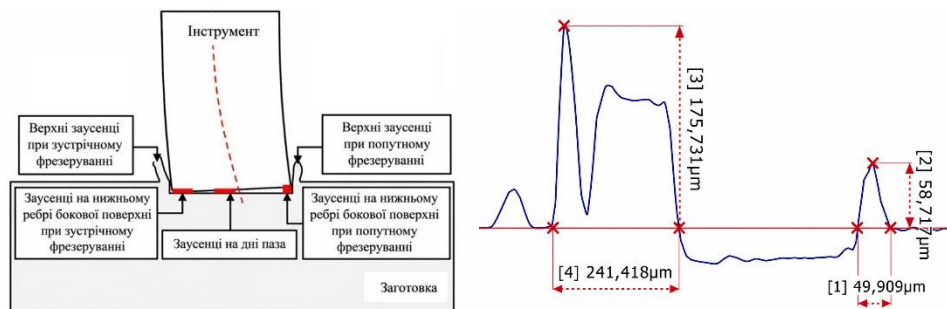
Формування заусенців та профіль поверхні паза при мікрофрезеруванні
